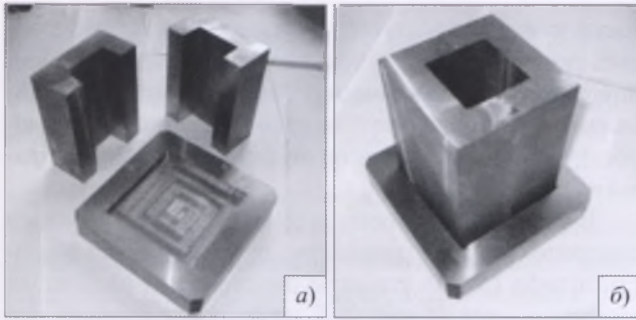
Кокиль для заливки экспериментальных образцов: а — части кокиля; б — кокиль в сборе
